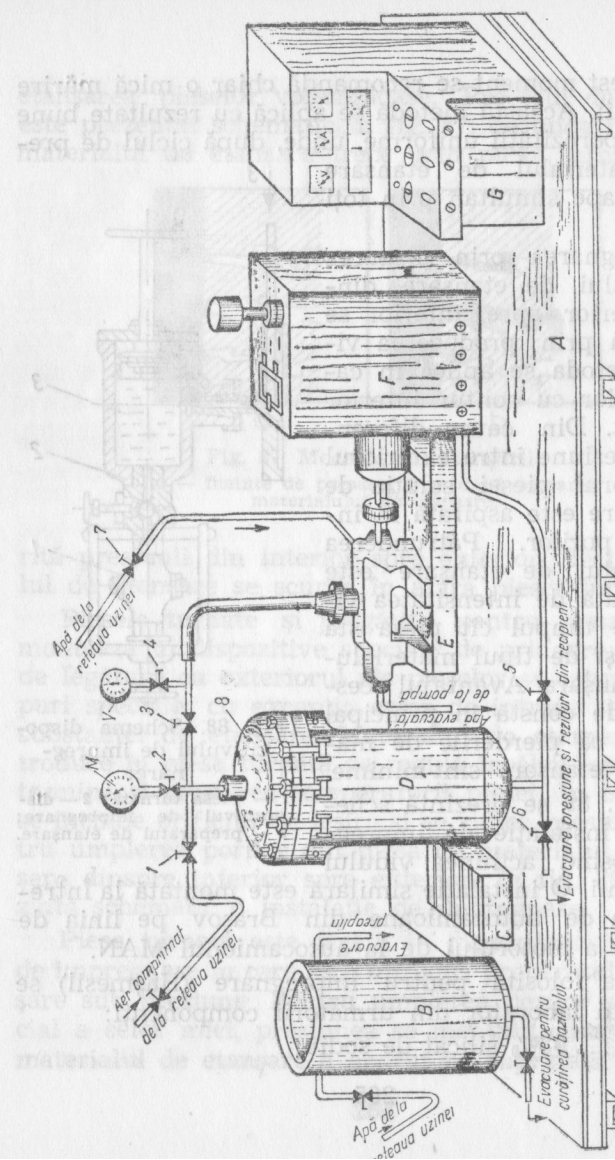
Instalație de impregnare prin vid și presiune: A — cadru metalic; B — bazin de spălare; C — grătar; D — recipient de impregnare; E — pompă de vid; F — ba-
